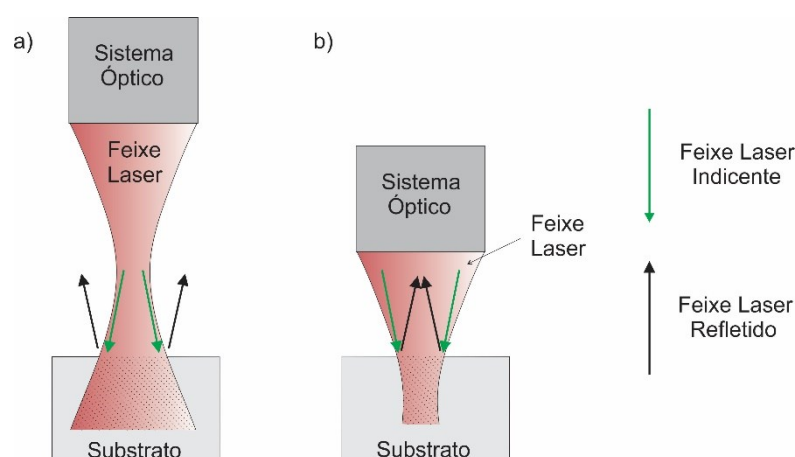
Posição do ponto focal do Laser (a) acima, e (b) abaixo da superfície da peça a ser soldada. (Fonte: Autor)
